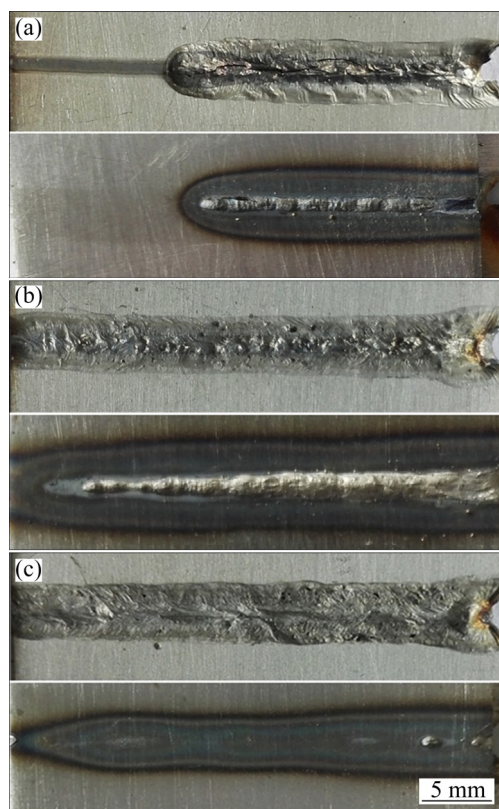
不同焊接工艺条件下铝/钢焊缝表面形貌
